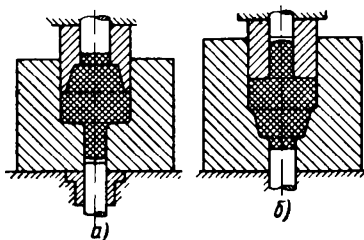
Схема штамповки поковки со ступенчатой конической головкой: а — неправильно; б — правильно
